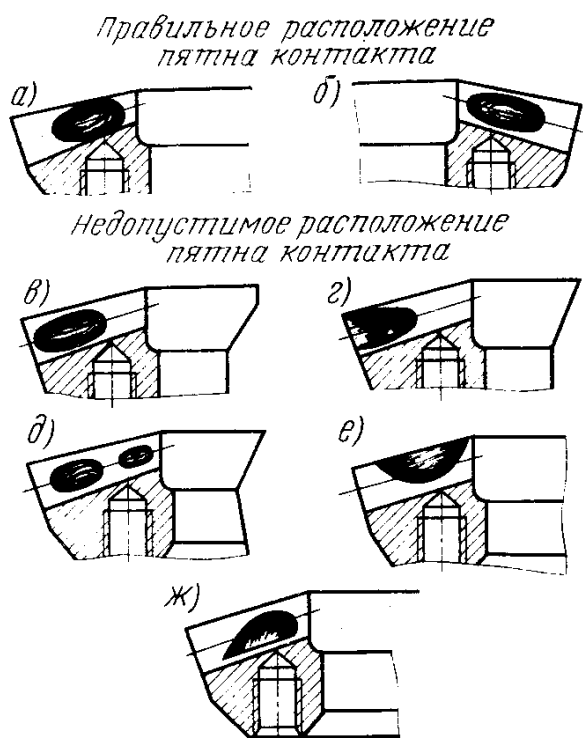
Расположение пятна контакта на зубьях ведомой шестерни главной передачи: а — пятно на стороне зуба, соответствующей движению автомобиля вперед; б — то же назад; в — пятно на внешней половине зуба; г — пятно выходит на внешний торец зуба; д — пятно раздвоено; е — пятно выходит на верхнюю кромку зуба; ж — пятно расположено у основания зуба; недопустимо также бегающее пятно контакта (восьмерка), вызываемое короблением зуба.
